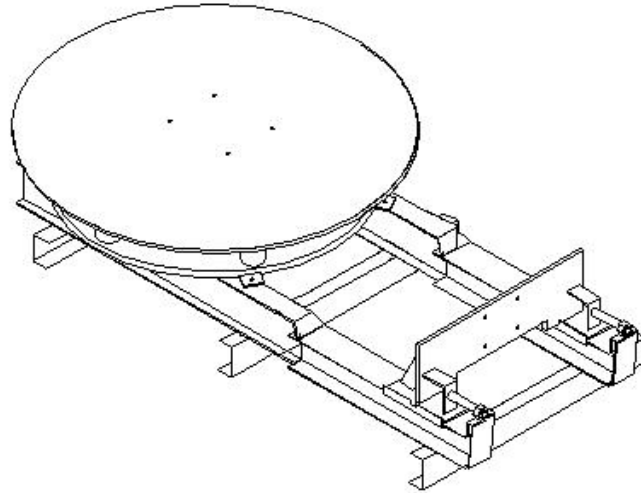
Mecanismo de rotación con las tres vigas de perfil UPN
